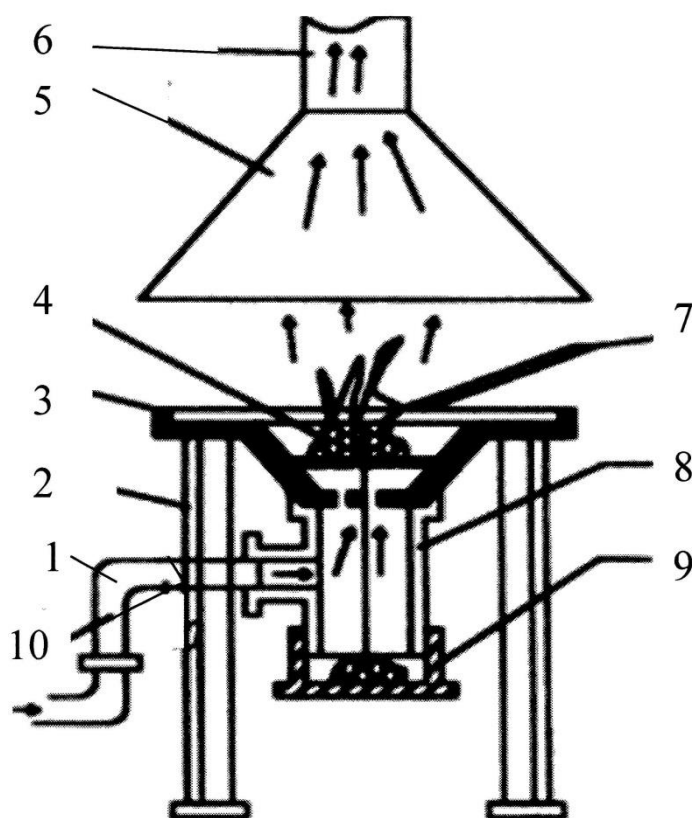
Схема устройства кузнечного одноместного открытого горна: 1 – труба воздушная; 2 – подставка; 3 – чаша чугунная; 4 – решётка чугунная; 5 – зонт вытяжной; 6 – труба дымовая; 7 – заготовка; 8 – фурма; 9 – крышка; 10 – заслонка
